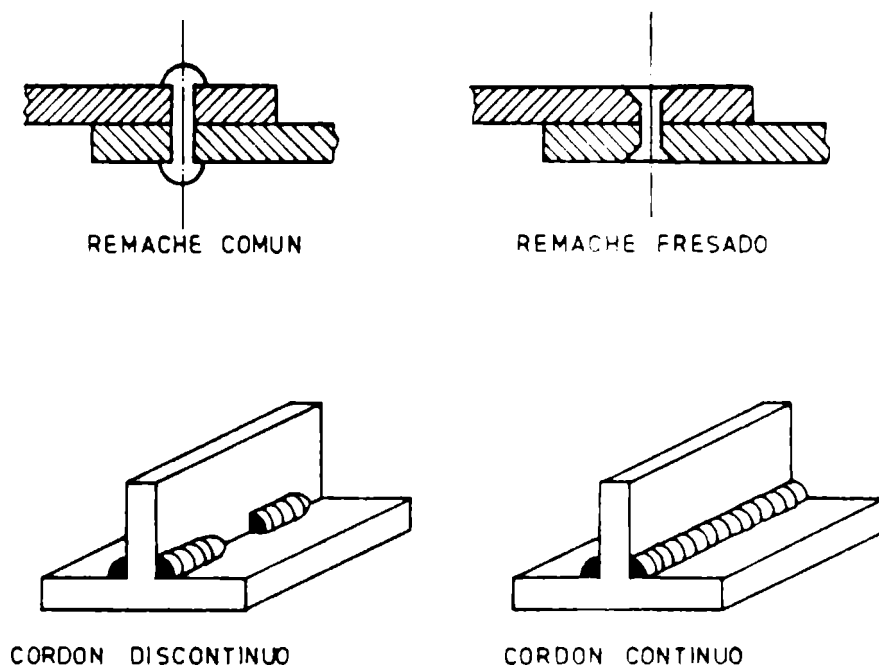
Diferentes tipos de remaches (común y fresado) y cordones de soldadura
